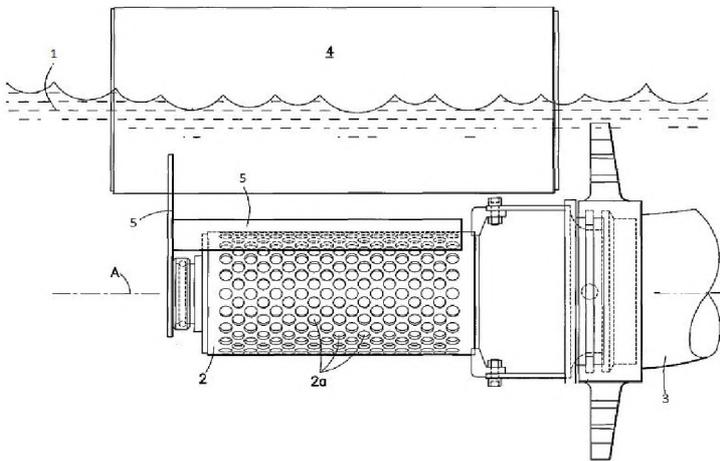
Конструкция плавающего устройства для всасывающей сетки:
